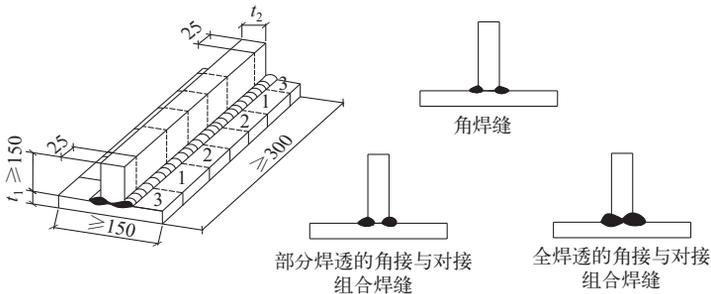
板材角焊缝和 T 形对接与角接组合焊缝接头试件及宏观试样的取样位置
